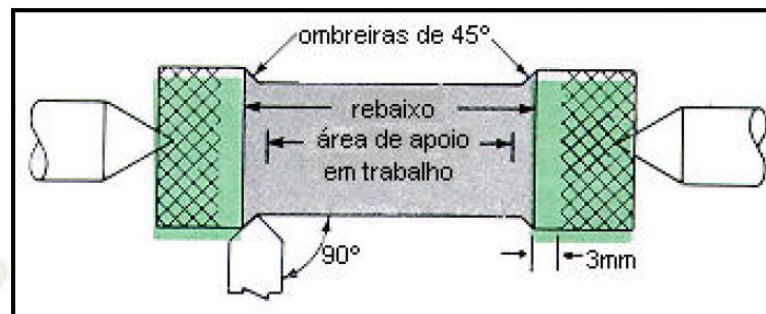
Mecanizado y reducción con herramienta de corte de 90°
